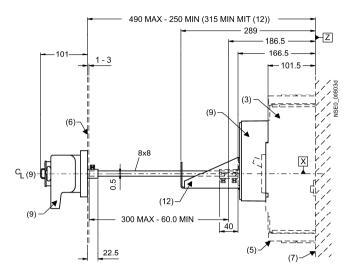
Neu_Frontansicht und Seitenansicht des Motorantrieb MO 3VL5 und 3VL6
